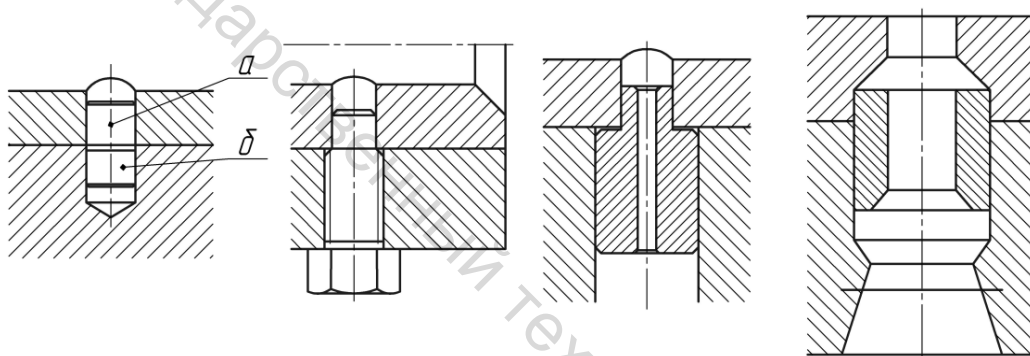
Установочные штифты вкладышей подшипников
